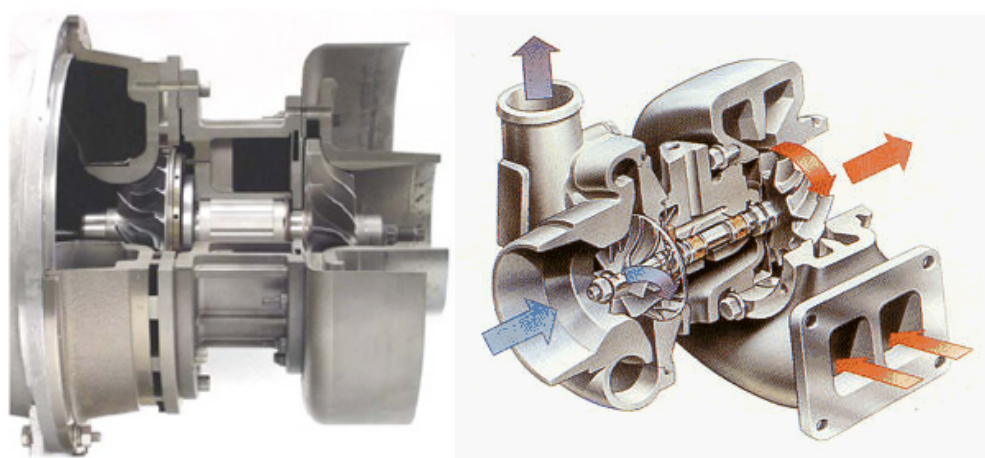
Системы с лепестковыми газодинамическими подшипниками
